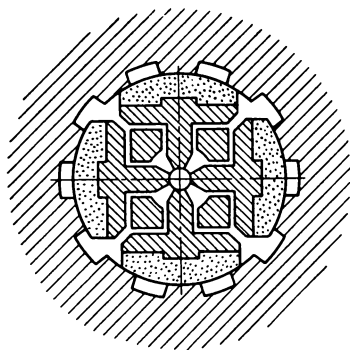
Схема операции хонингования внутренней цилиндрической поверхности шлицевого отверстия
